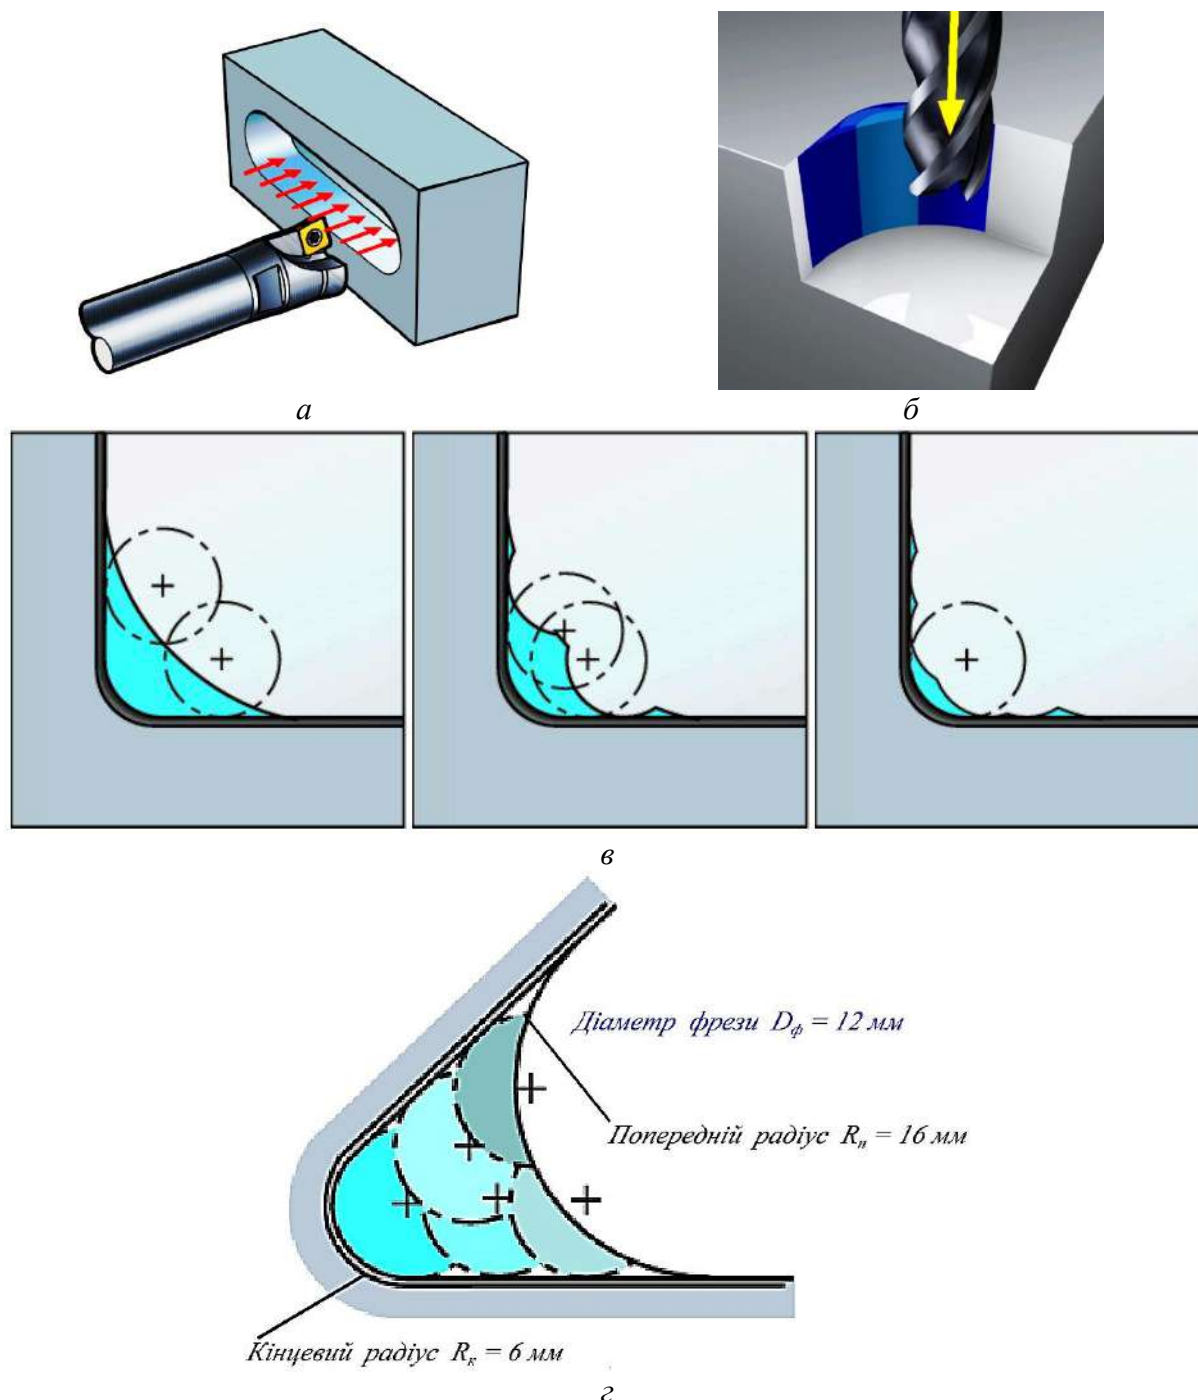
Оброблення карманів, глибоких закритих пазів і кутів плунжерним фрезеруванням: а – схема оброблення паза; б – загальна схема оброблення кута; в – схема оброблення прямого кута; з – схема оброблення гострого кута
